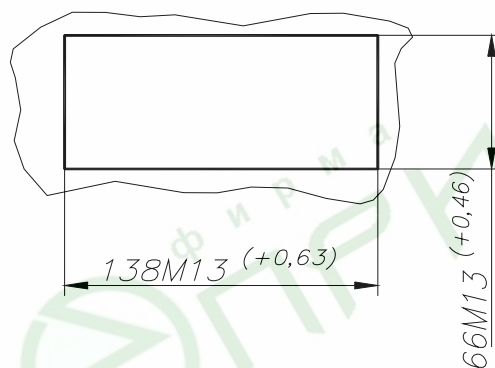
Габаритные и присоединительные размеры прибора
